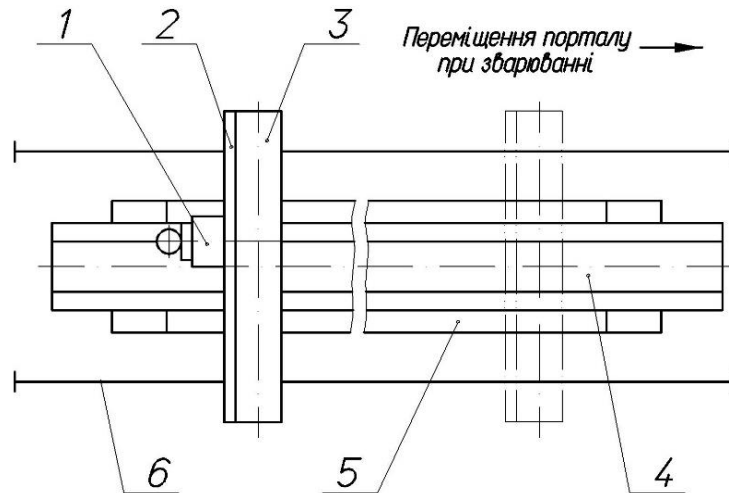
Схема зварювання балки при переміщенні порталу зі зварювальним автоматом зі швидкістю зварювання:
